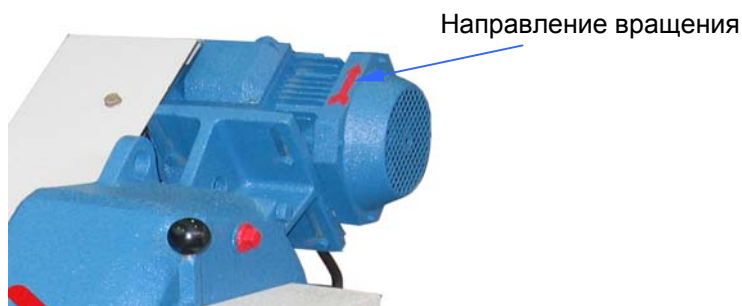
Стрелка, указывающая направление вращения двигателя
